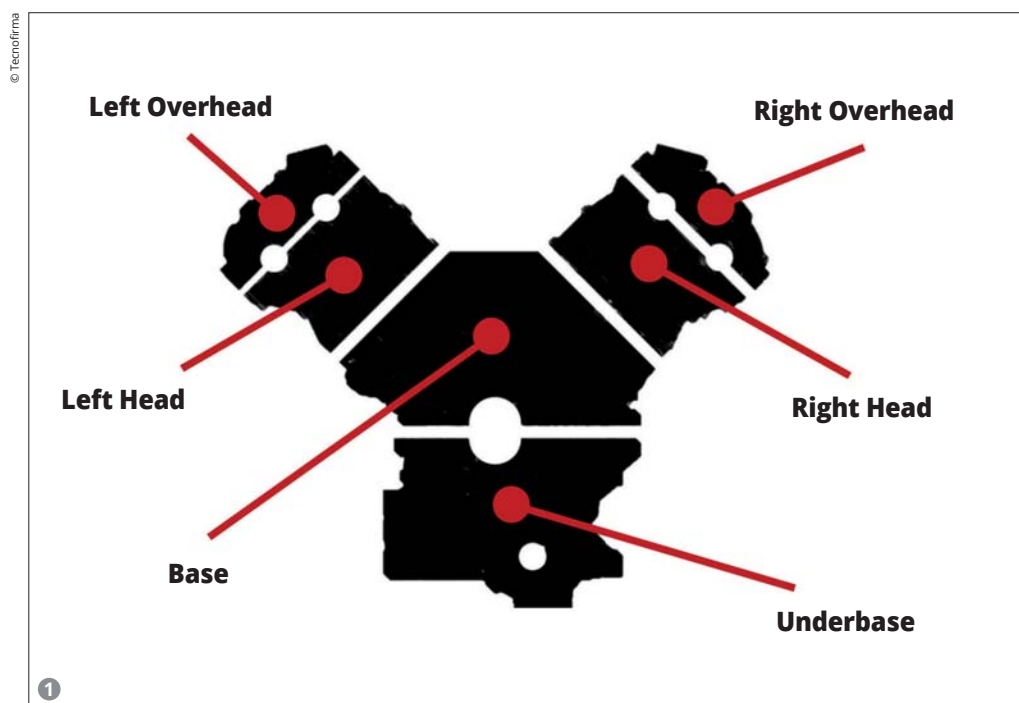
Disegno della composizione del motore a 6 cilindri lavato nell'impianto di Tecnofirma.
